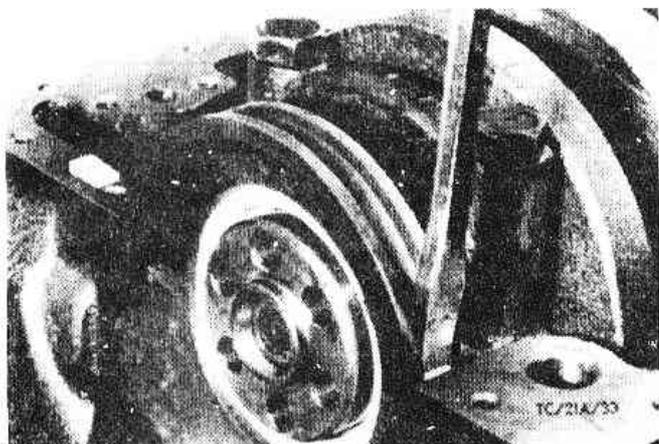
В.15. Установка сухарей заднего коренного подшипника (Разд.26)
